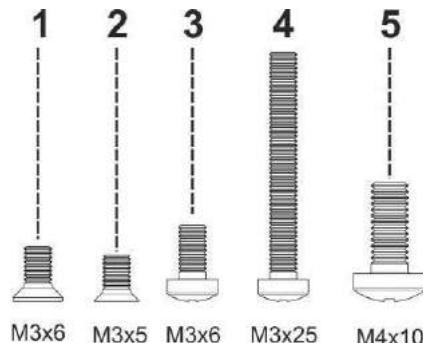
Типы болтов для сборки TAU-72.IP/TAU-36.IP
